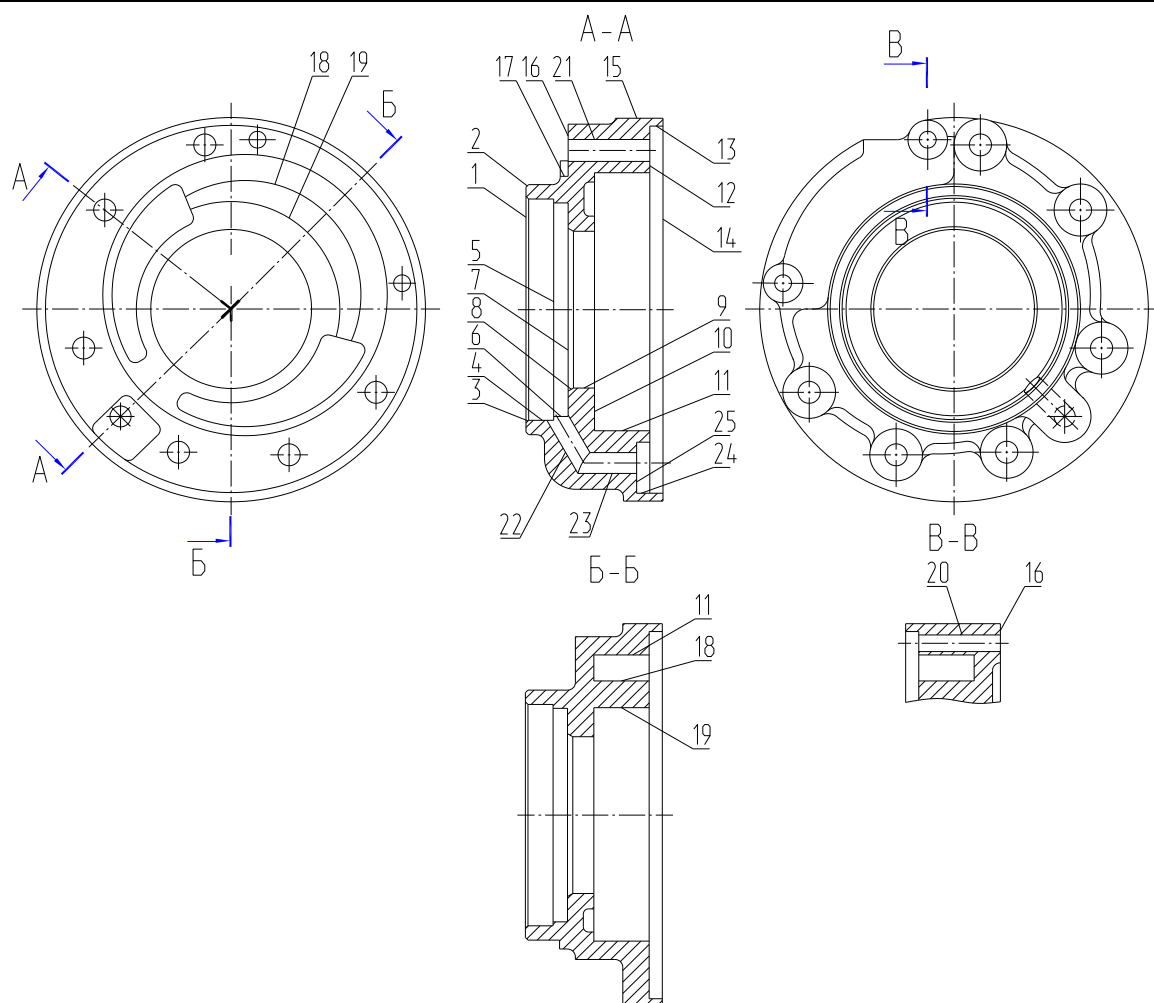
Систематизация поверхностей детали «Корпус насоса гидрокоробки»
